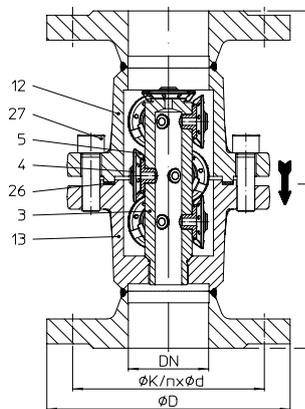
1....10K2 (DN40-50) com 10 cápsulas, com flanges em linha
